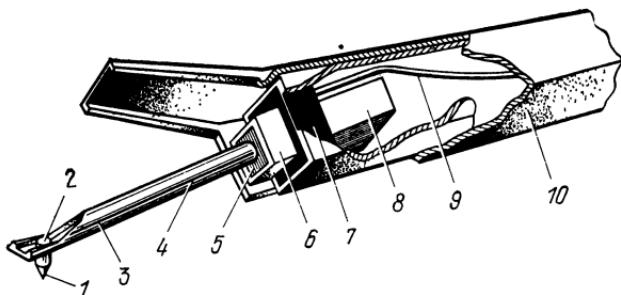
Конструкция вставки для звукоснимателя с подвижным магнитом:
